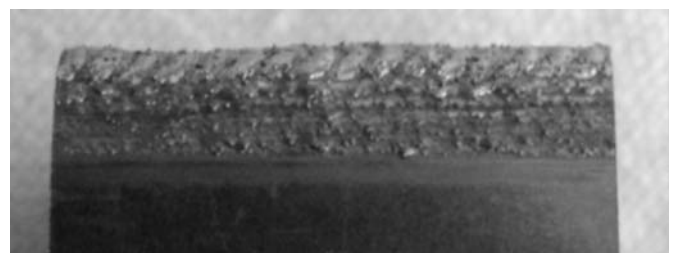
Образец с наплавкой на торцевой поверхности материала Ti6Al4V
